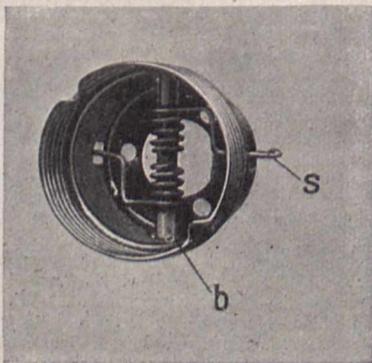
Fassungsboden mit Schraubenfeder aus Stahldraht (s), b = Bolzen.
